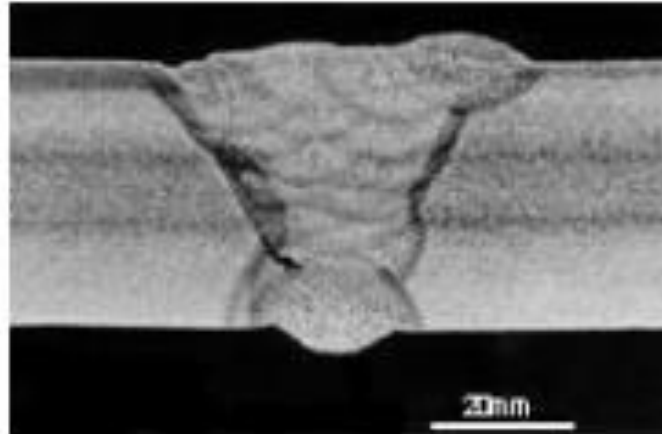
Manque de fusion dans le flanc de la soudure.
